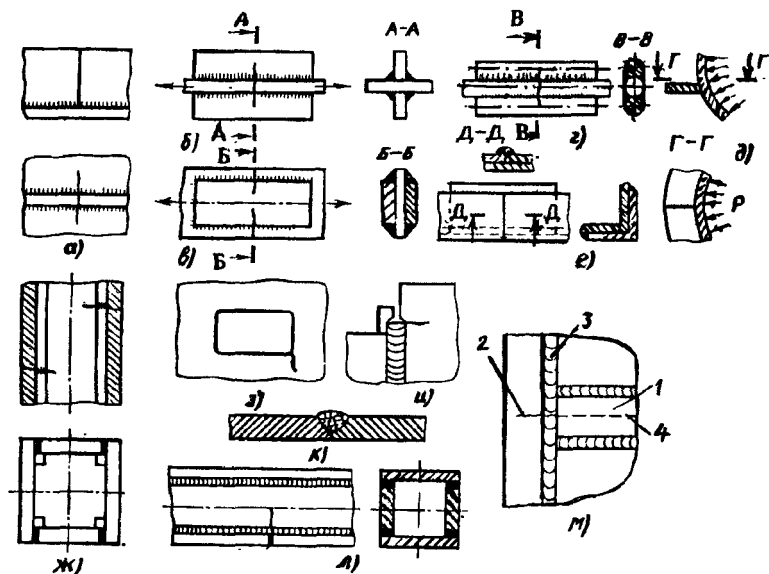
Примеры разрушений в сварных конструкциях
